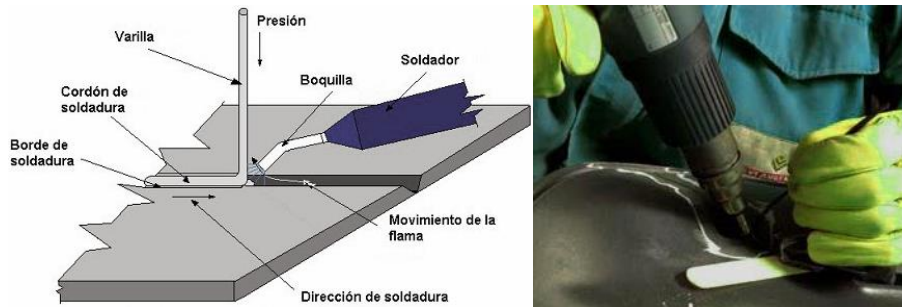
Esquema del método de soldadura por aire caliente y su aplicación [10].
